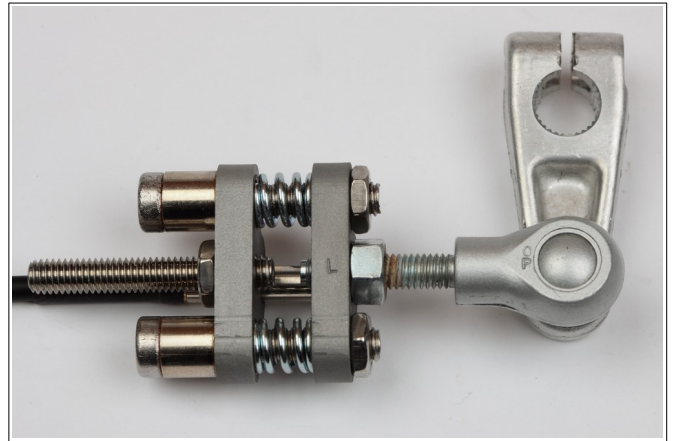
Magnetplatte mit M6-Linksgewinde.
